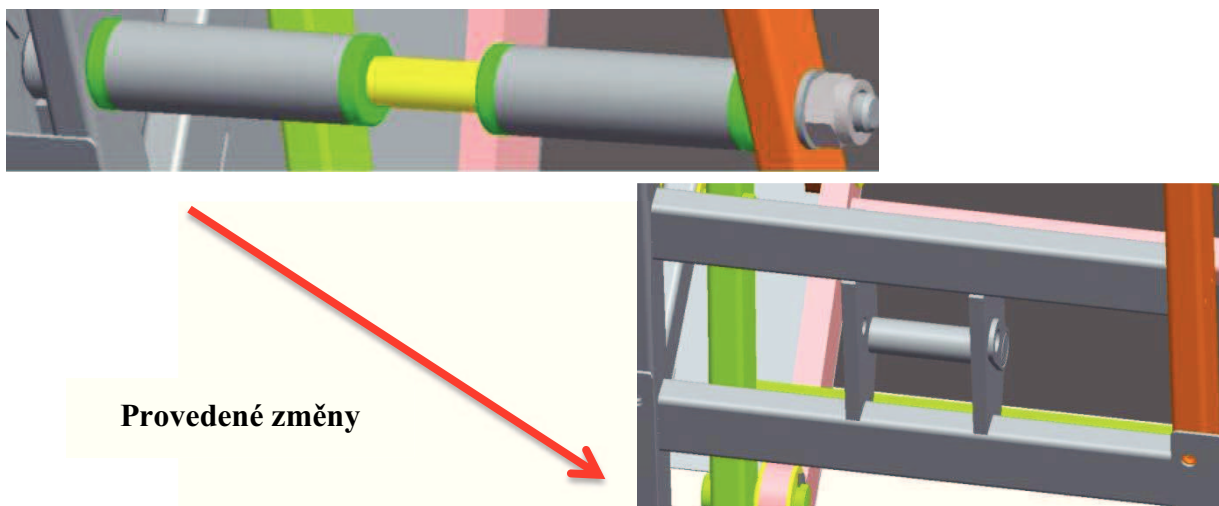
Nová konstrukce pevného úchytu zadní části motoru č. 1
